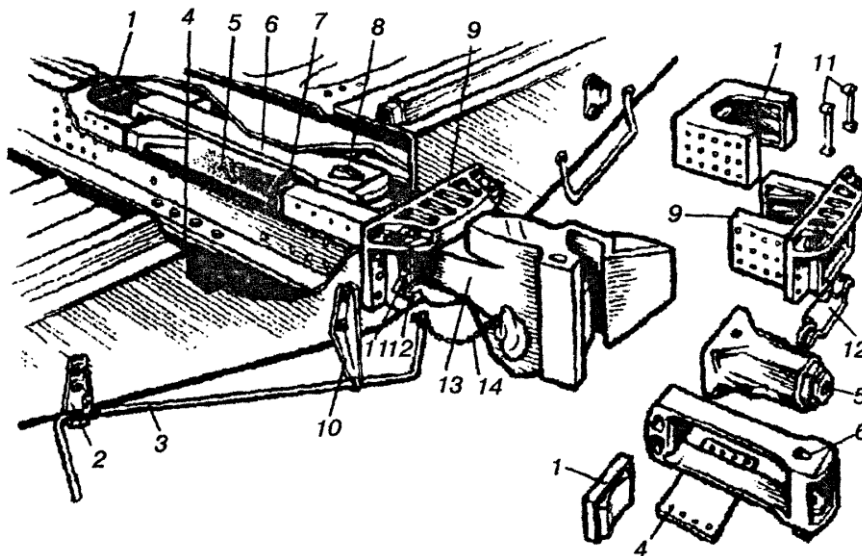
Автосцепное устройство вагонного типа и его детали
